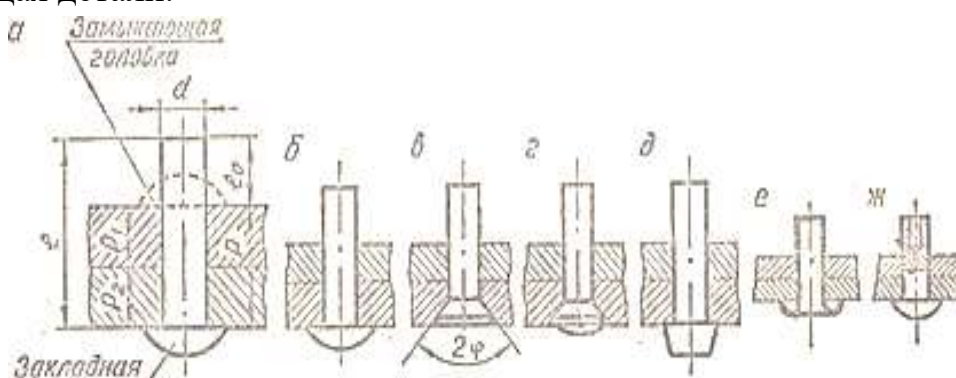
Элементы заклепочного соединения и виды заклепок
